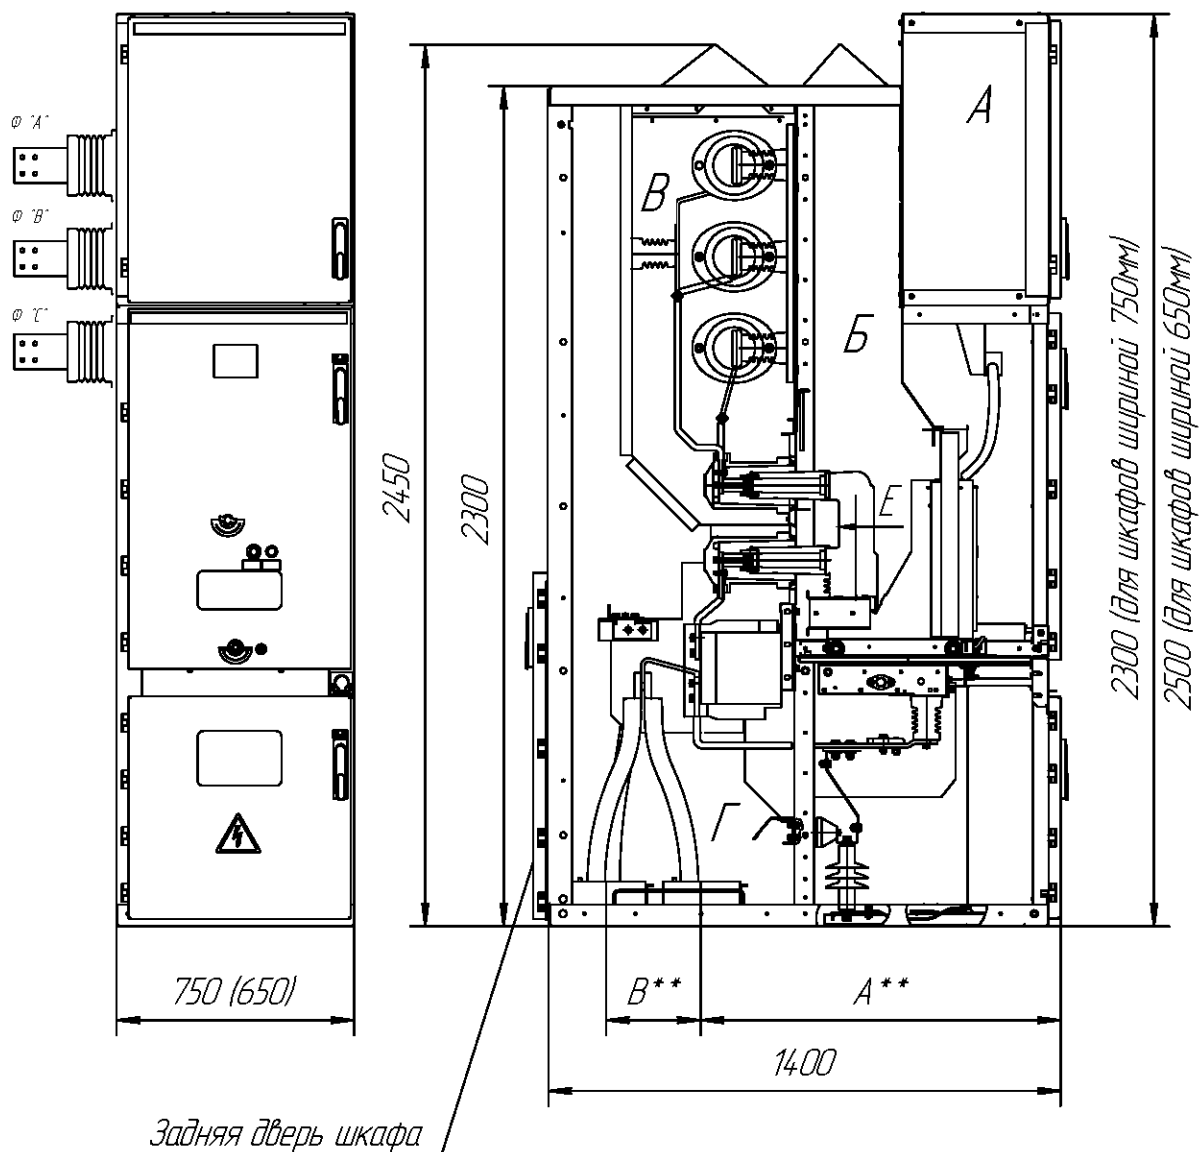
Габаритные , установочные, присоединительные размеры шкафов
